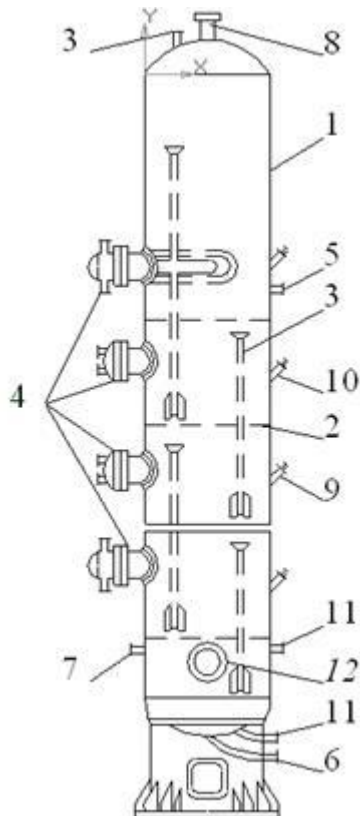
Колонна окисления изопропилбензола: 1 – корпус; 2 – тарелка; 3 – переливная трубка; 4 – встроенный теплообменник; 5 – штуцер для входа питания; 6 – штуцер для выхода реакционной массы; 7 – штуцер для входа воздуха; 8 – штуцер для выхода газа; 9 – штуцер для продувки; 10 – штуцер для термомпары; 11 – штуцер для мерного стекла; 12 – лаз
